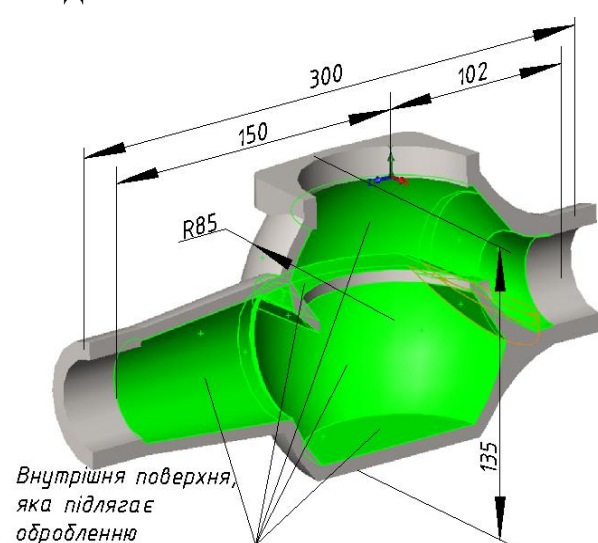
Загальний вигляд корпусу водолічильника KB-10 з виділеною внутрішньою поверхнею, що підлягає обробленню (переріз)
